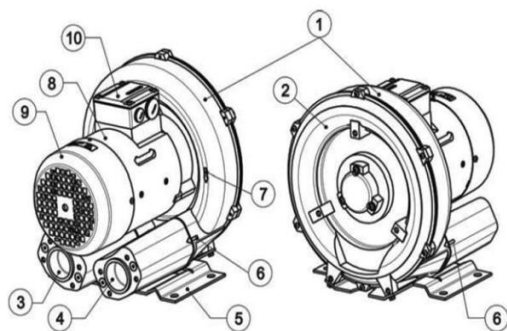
Конструкция вакуумного насоса/компрессора с боковым каналом
